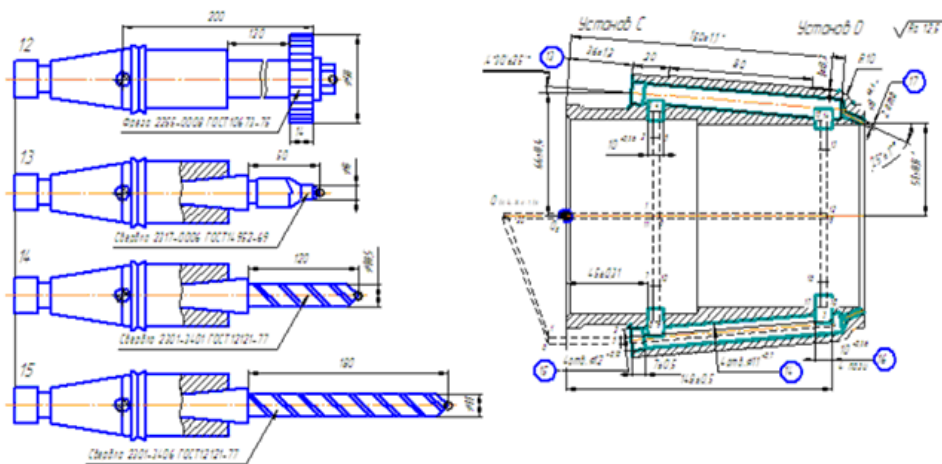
Наладка станка IP500МФ4 на изготовление цилиндра перфоратора ПТ48А (операции 1-11)
